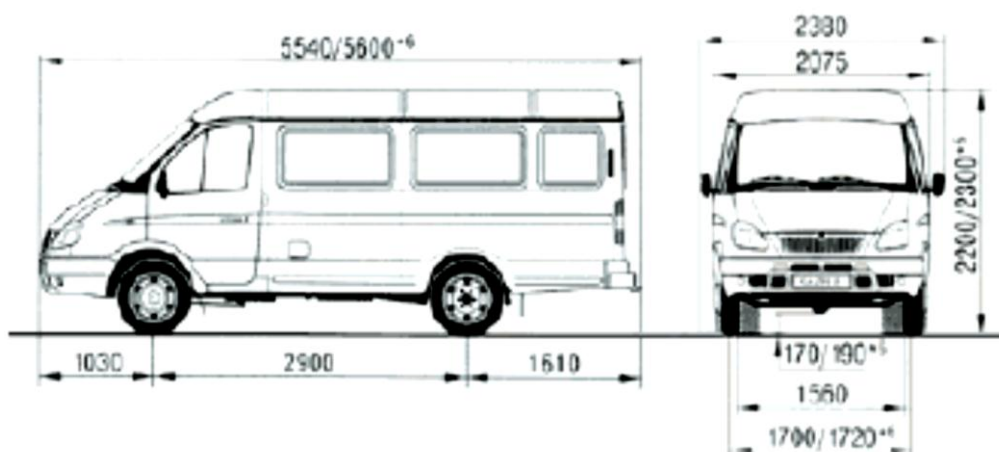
Общий вид и габаритные размеры ГАЗ-322132
